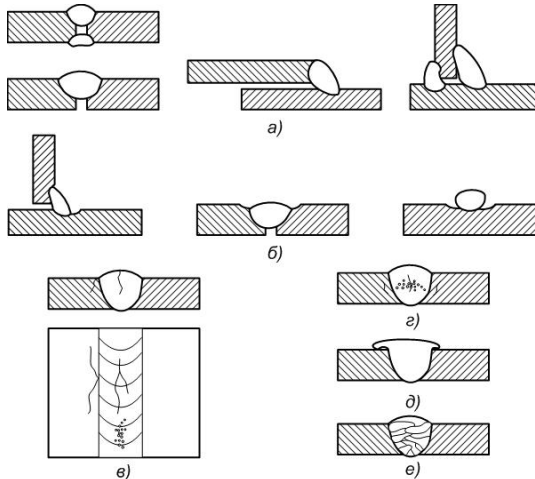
Виды дефектов в сварных соединениях: а) непровар; б) подрезы; в) наружные трещины и поры; г) внутренние трещины и поры; д) наплыв; е) шлаковые включения.
